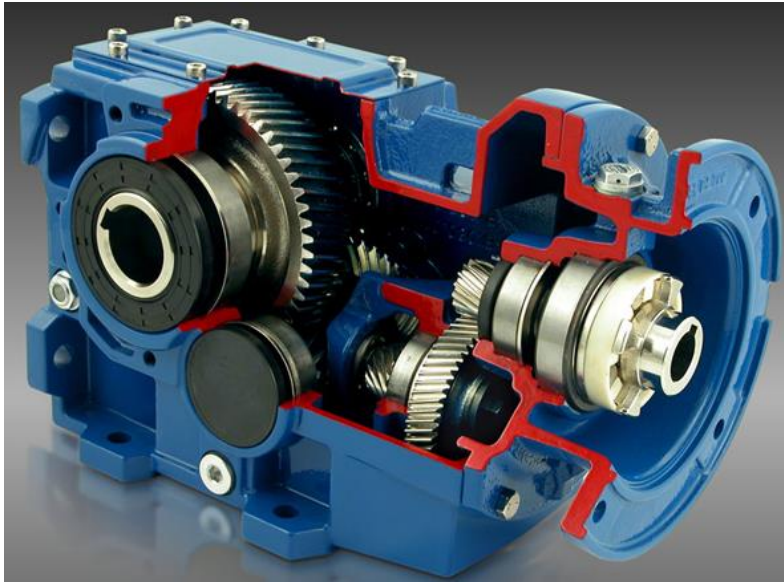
Premium Planetary Gear Motor 313 RPM HD
